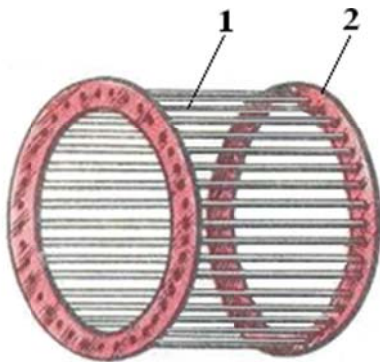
Сварная короткозамкнутая обмотка ротора типа «беличьей клетки». 1 – стержень; 2 – короткозамыкающее кольцо
